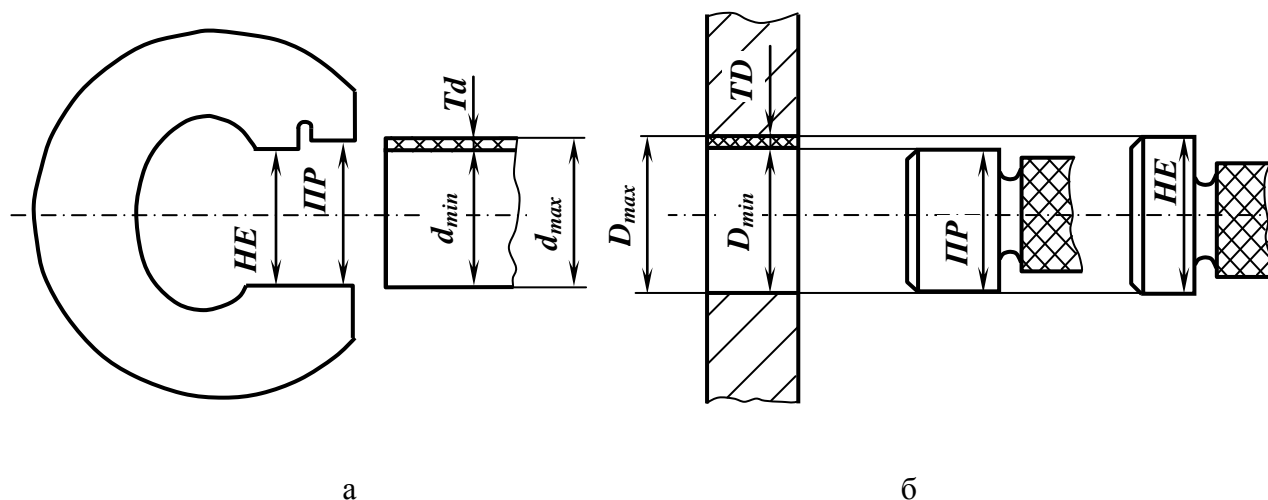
Схемы контроля деталей: а – вала скобой; б – отверстия пробками
